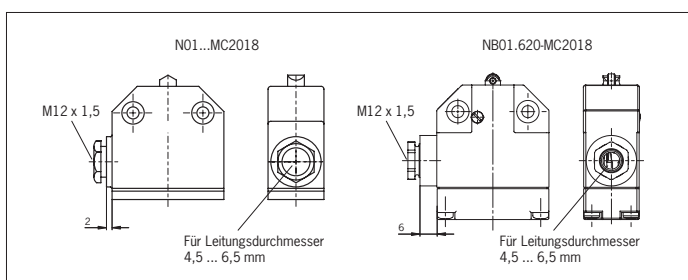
Maßzeichnung N01...MC2018/NB01.620-MC2018 mit Halbverschraubung
